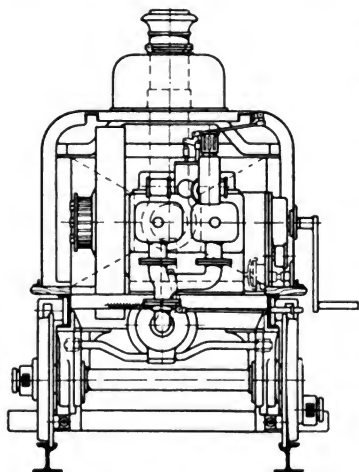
Motorlokomotive der Wolsley Tool and Motor Car Works in Birmingham.
